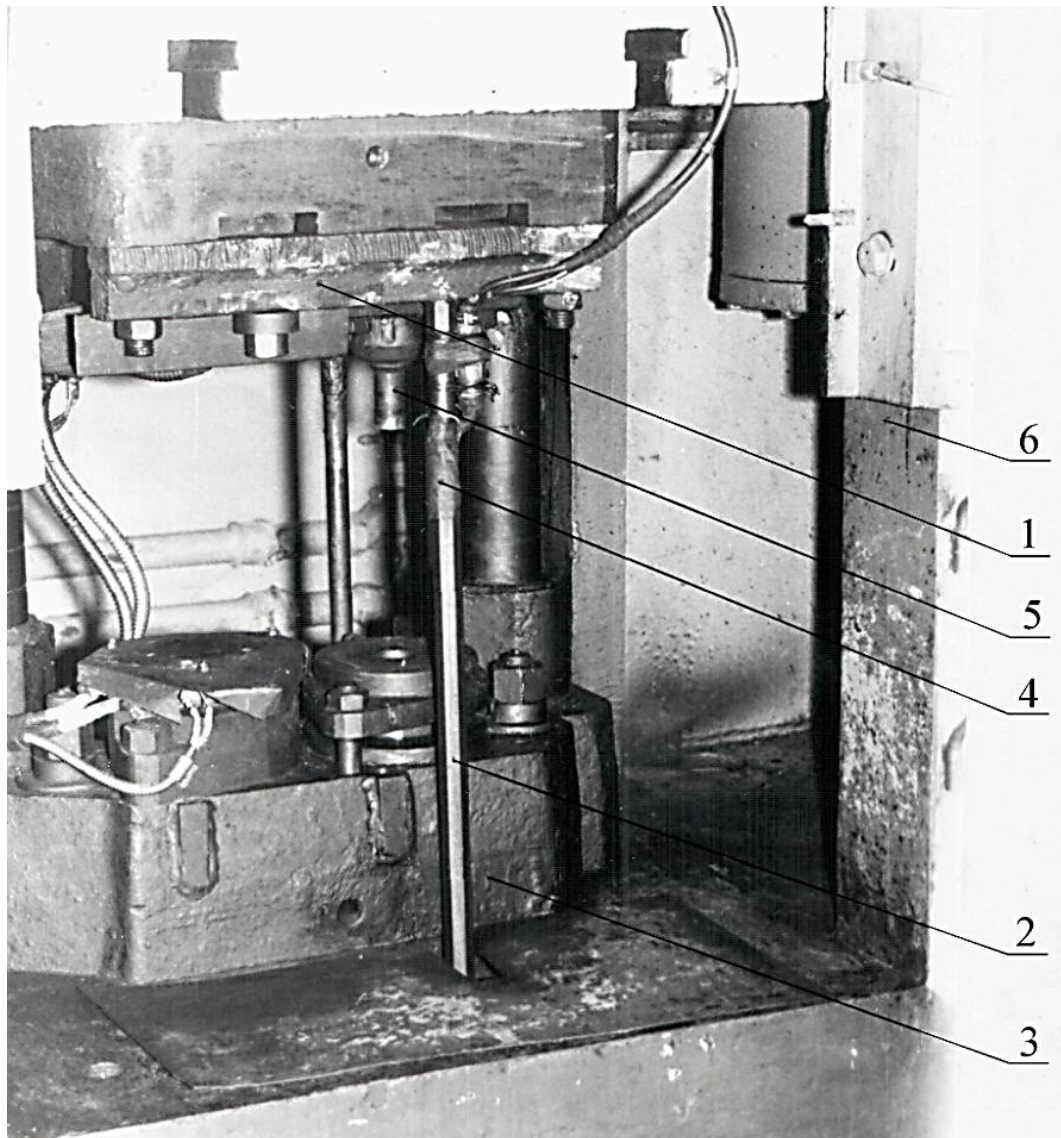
Лабораторная установка для штамповки автомобильных клапанов (1 – соединительная планка; 2 – тяга вертикальная; 3 – штамп; 4 – тензометрические датчики; 5 – пуансон; 6 – пресс)
